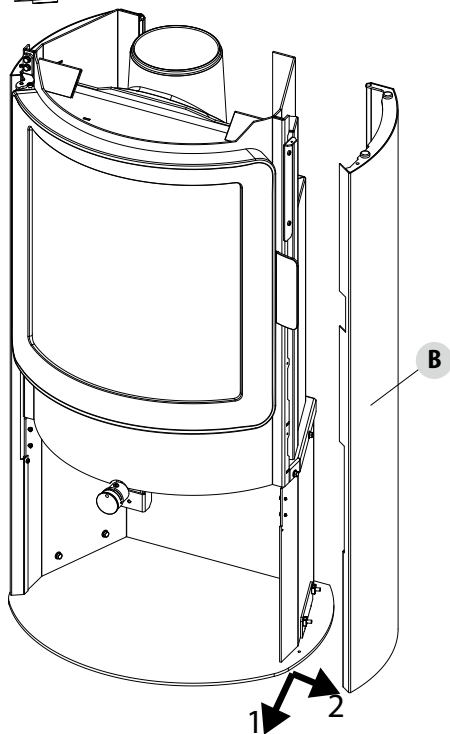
PANNELLO FRONTALE - SMONTAGGIO
